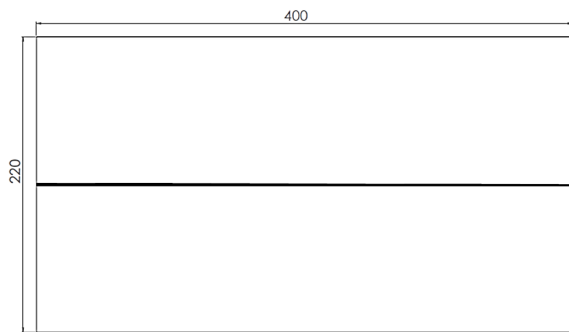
Lámina soldada a utilizar en procedimientos experimentales
